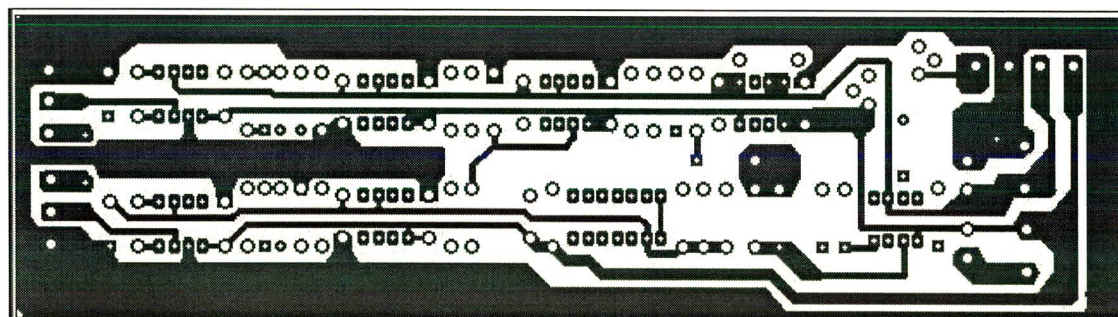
Lay-out das ligações da placa - lado da solda (visto pelo topo)
